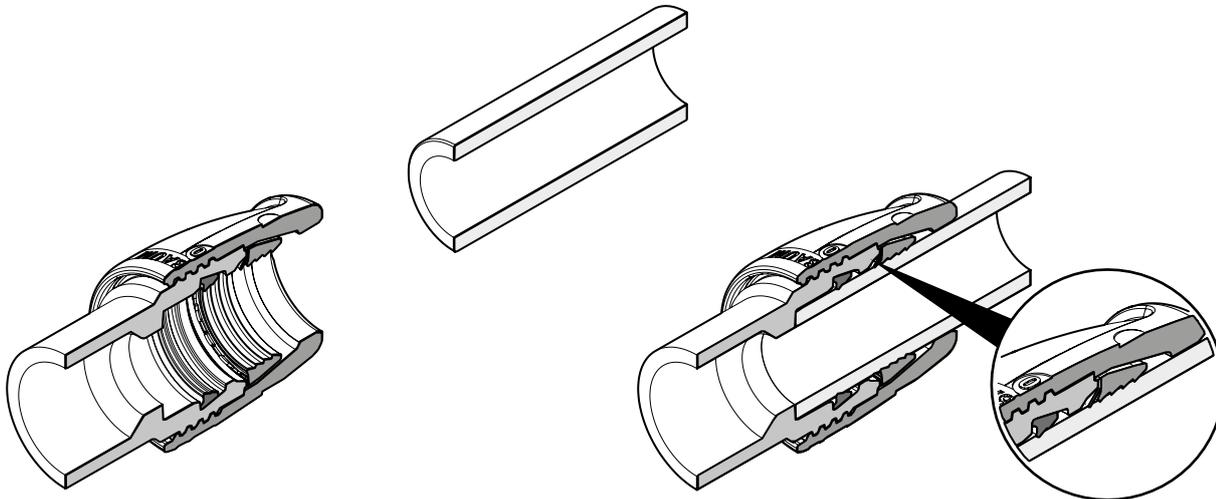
Assemblage Optiflex-Profix (ouvert/emboîté)
